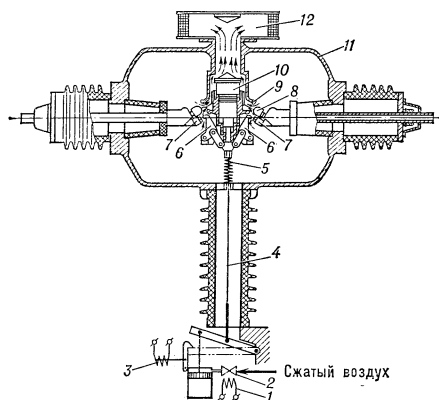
Принципиальная схема воздушного выключателя с закрытым отделителем: 1 — электромагнит включения; 2 — клапан подачи сжатого воздуха; 3 — электромагнит выключения; 4 — изоляционная штанга; 5 — пружина; 6 — подвижные контакты; 7 — неподвижные контакты; 8 — дугоприёмные электроды; 9 — сопло; 10 — клапан выпуска; 11 — резервуар; 12 — газоотводный канал.
